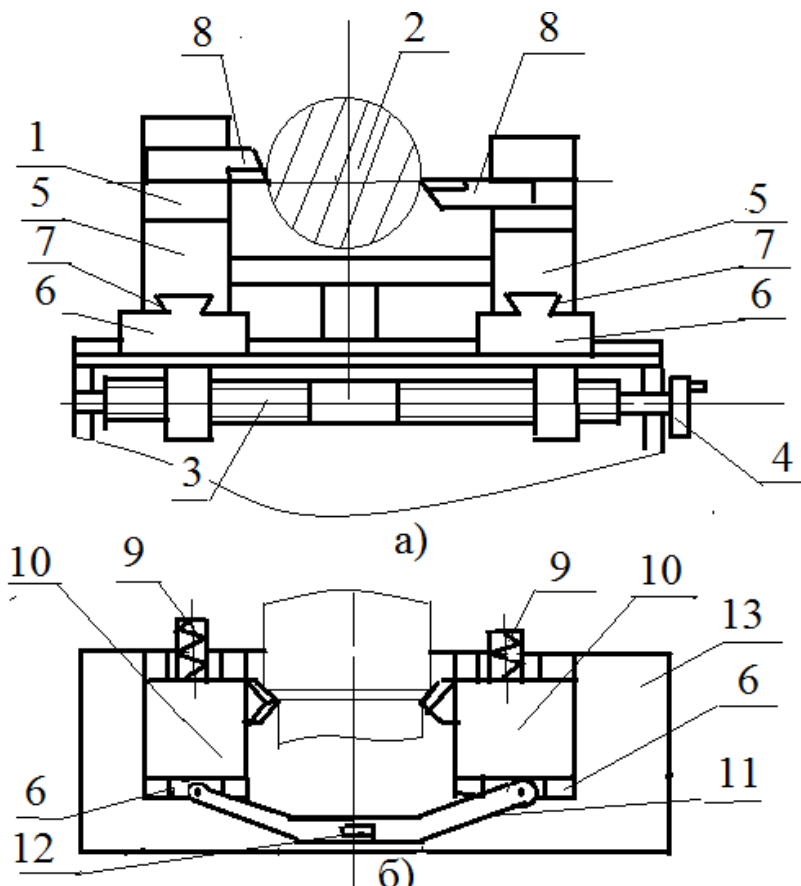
Самоналагоджувальний дворіздцевий супорт з між інструментальним кінематичним зв'язком
